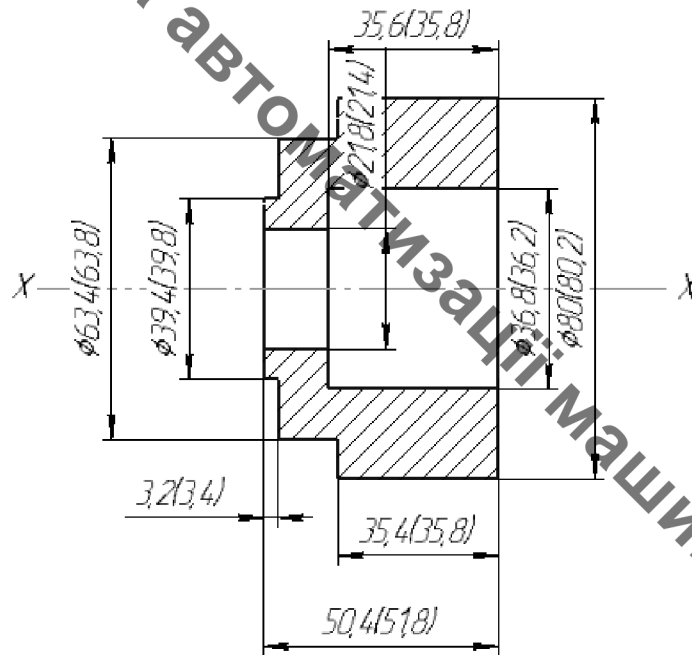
Ескіз заготовки виготовлений литтям в піщано-глинисті форми та оболонковій
